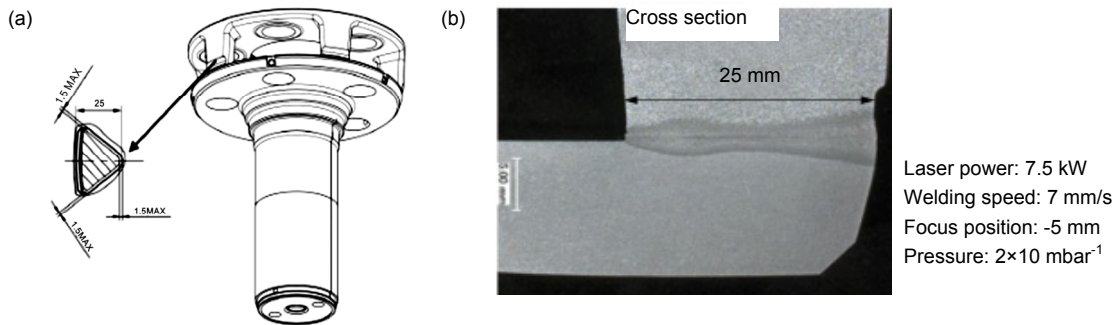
大型齿轮真空激光焊接<sup>[30]</sup>. (a) 焊接位置示意图. (b) 焊缝横截面.
